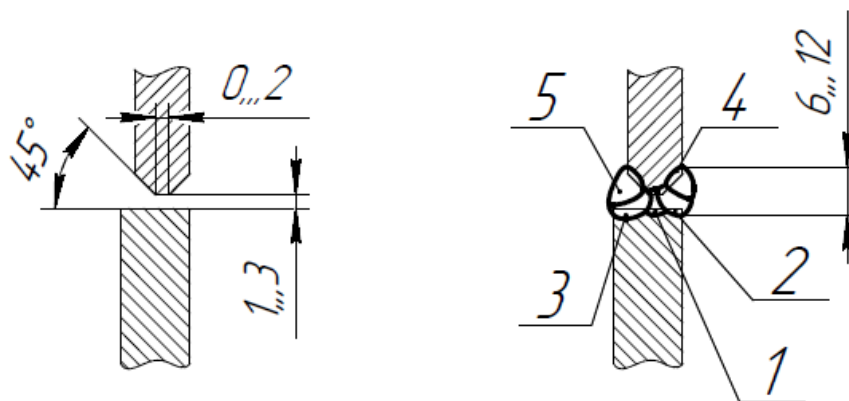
Сварка горизонтального сварного шва
